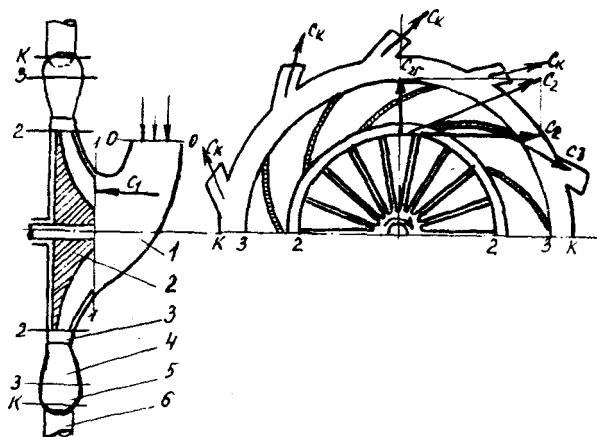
Принципиальная схема устройства центробежного нагнетателя: 1—входной патрубок; 2—крыльчатка; 3—безлопаточный диффузор; 4—лопаточный диффузор; 5—сборник-распределитель смеси; 6—выходной патрубок
